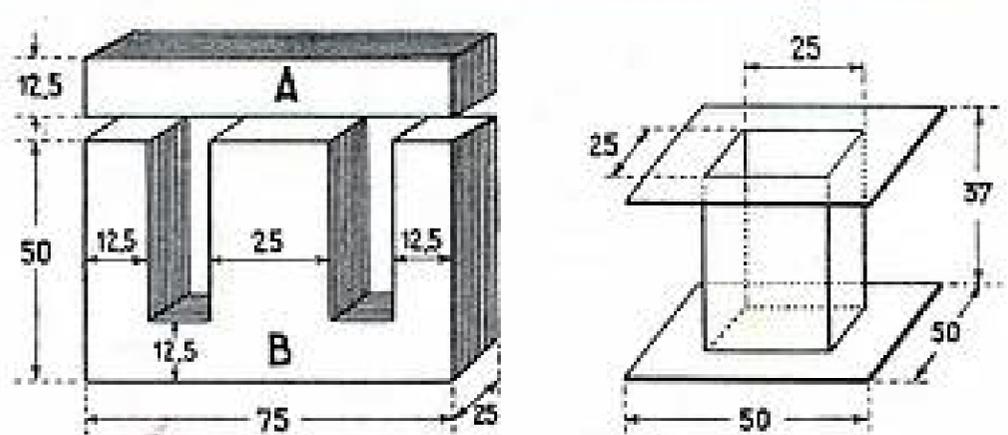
Dimensions de la carcasse et du circuit magnétique pour la construction d'un bon transformateur de sortie.
